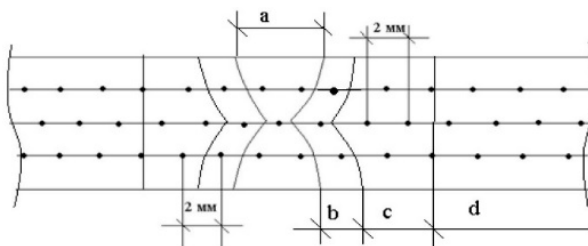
Схема проведения измерений твердости в сварном соединении
